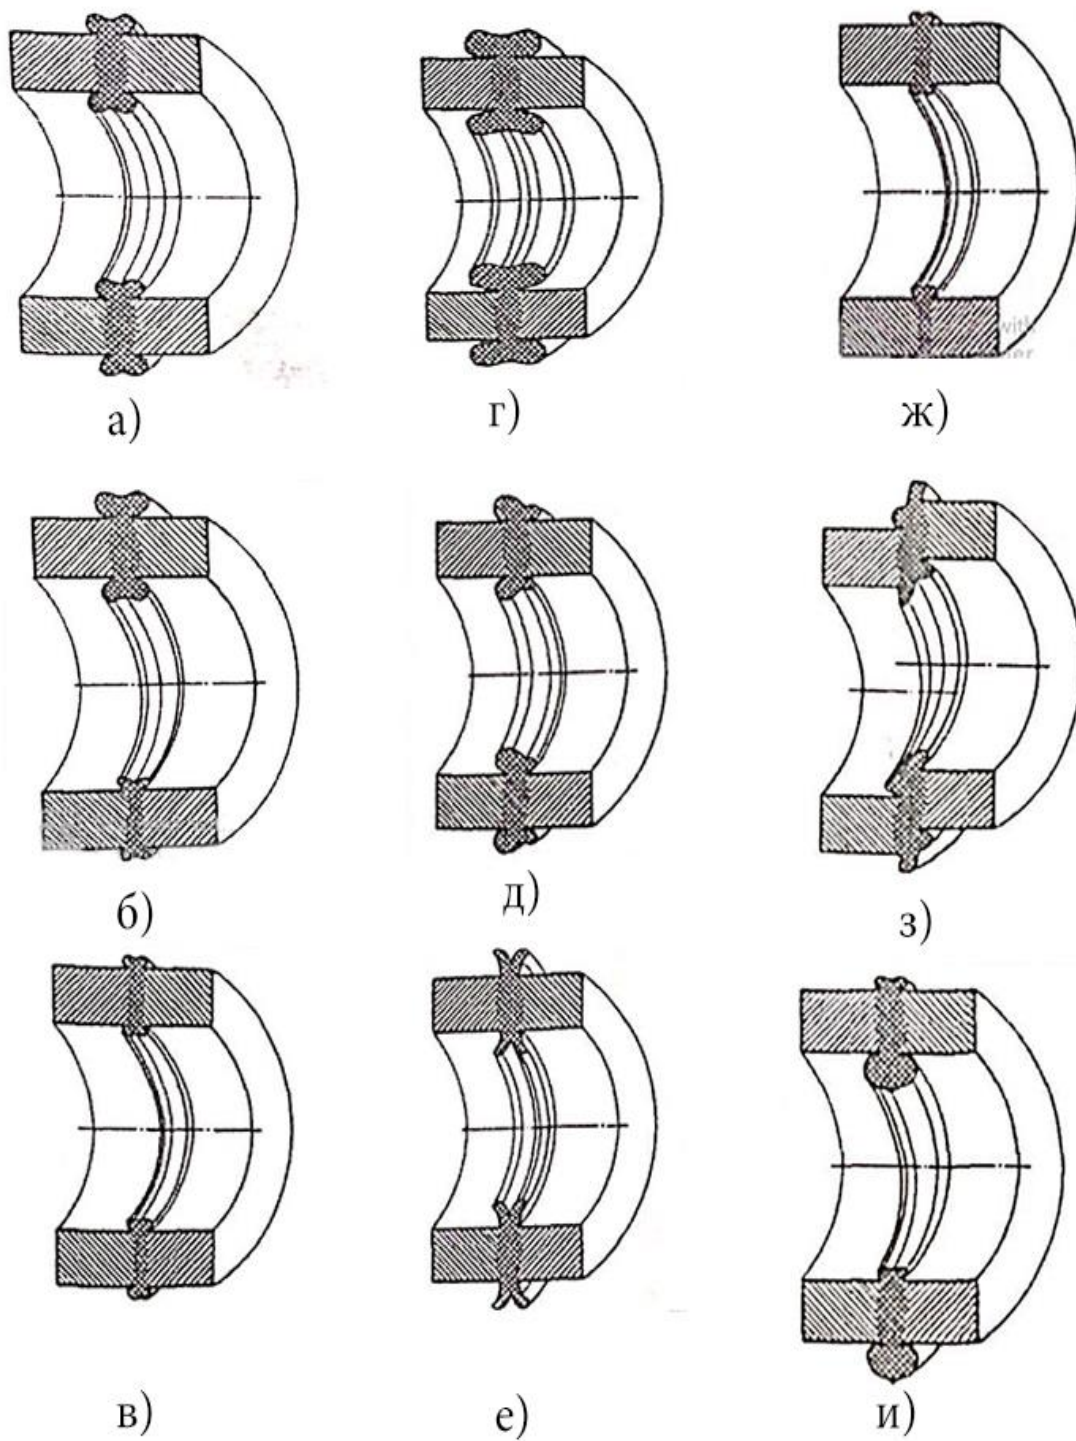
Внешний вид годных (а) и с браком (б-и) сварных соединений
